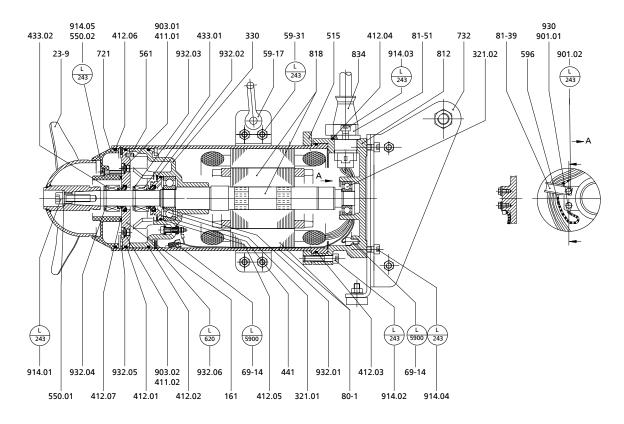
Чертеж общего вида Amamix 200, материал корпуса двигателя – высококачественная сталь
